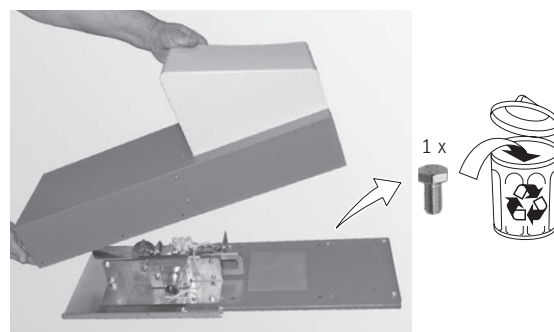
Abdeckung abheben und rot markierte Schraube entfernen
